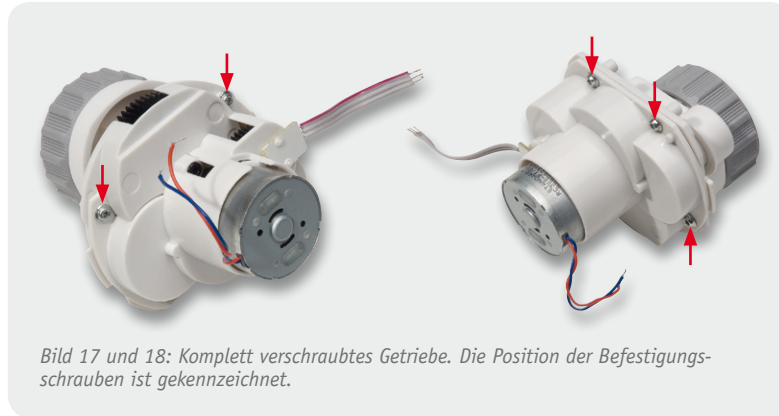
und 18: Komplett verschraubtes Getriebe. Die Position der Befestigungsschrauben ist gekennzeichnet.
